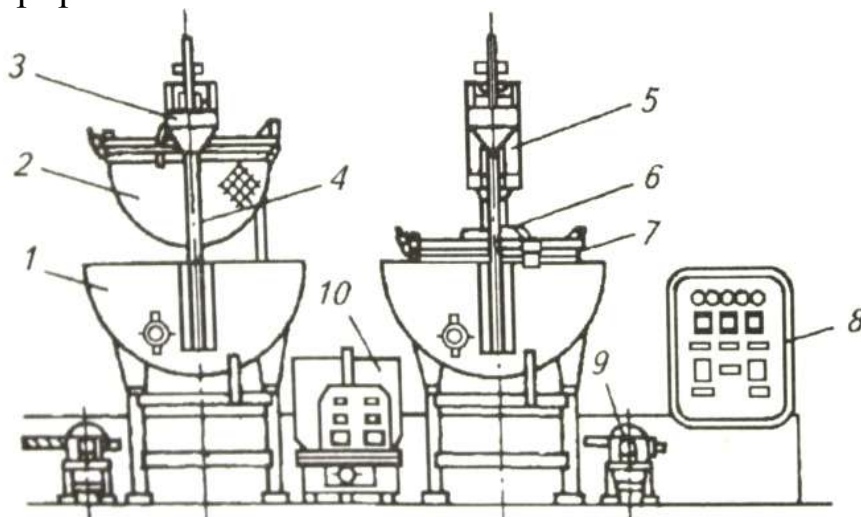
Творогоизготовитель с прессующими ваннами:
